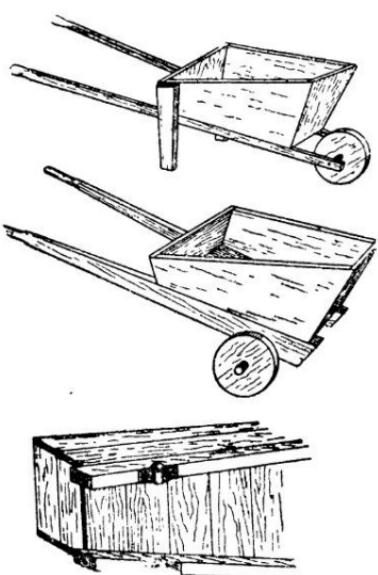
Одноколесная и двухколесная тачка (внизу — крепление оси к основным бруском).
